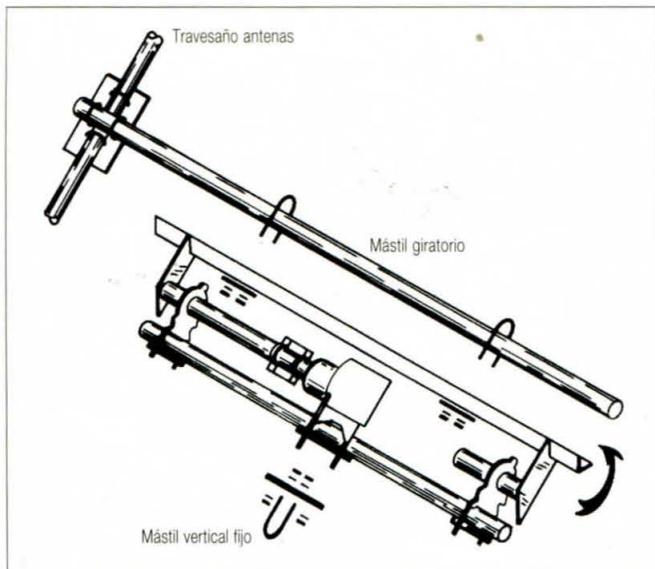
Visión de conjunto básica del sistema de elevación (véase el texto para los detalles constructivos).
